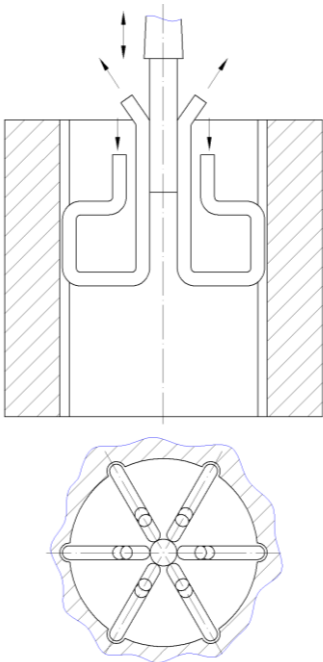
Індуктор для гартування півкруглих шліцевих поверхонь на шість позицій з окремими камерами
